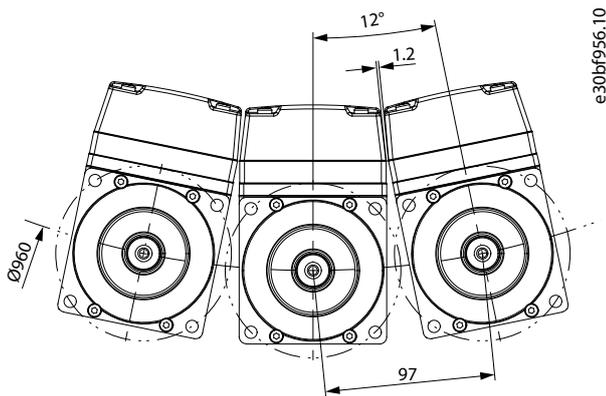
Esempio di installazione di servozionamento sulla stessa flangia
